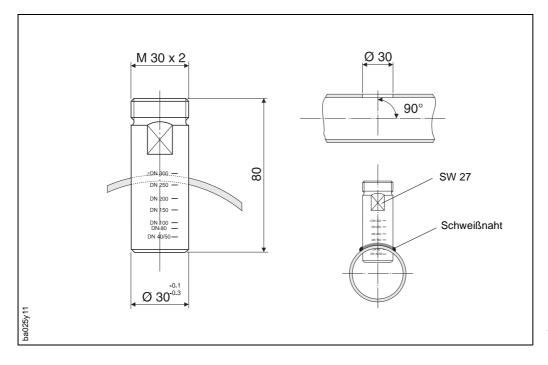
Einschweißstutzen ≥DN 40
